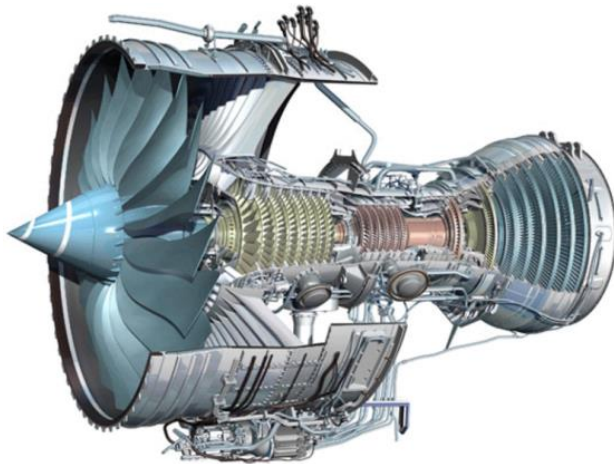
Общий вид современного газотурбинного двигателя (ГТД)
